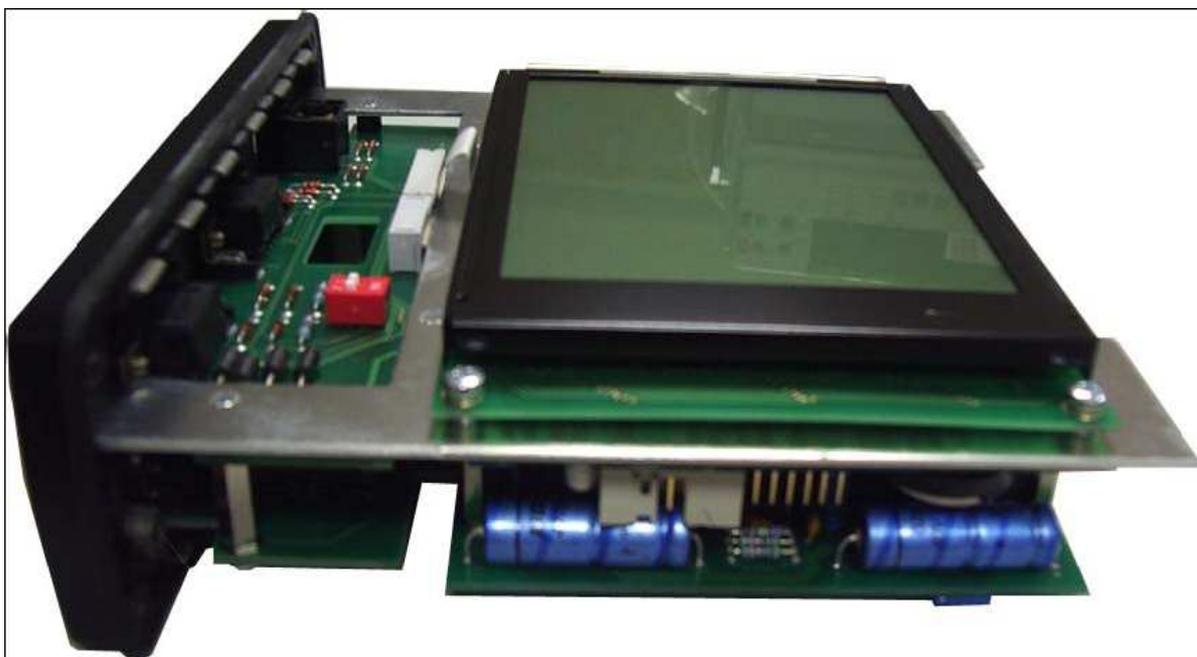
Конструктивное исполнение терминала для кабины ТЗ
